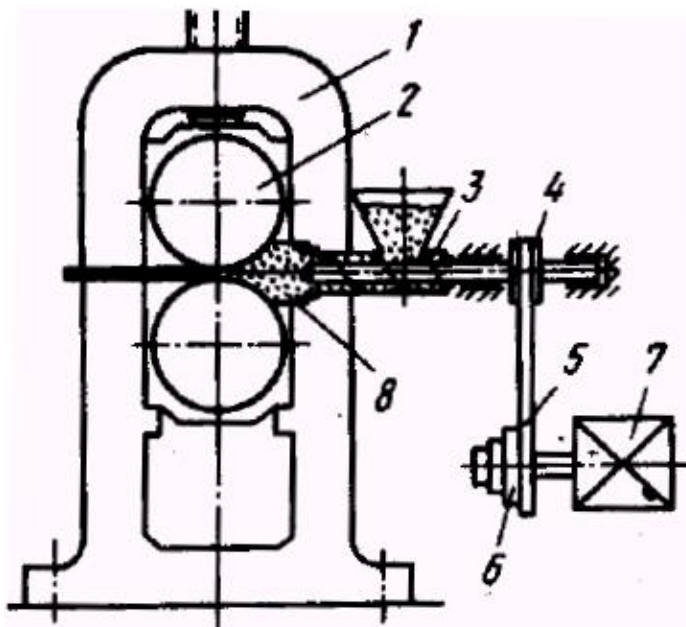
Прокатная клетка стана дуо для горизонтальной прокатки порошка с устройством его подачи: 1 – станина; 2 – рабочий валок; 3 – шнек; 4 – ведомый шкив; 5 – ремень; 6 – ведущий шкив; 7 – электродвигатель
